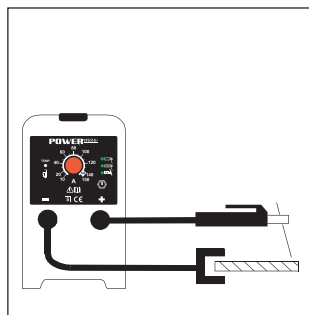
POWERmax équipé pour le soudage à la baguette
